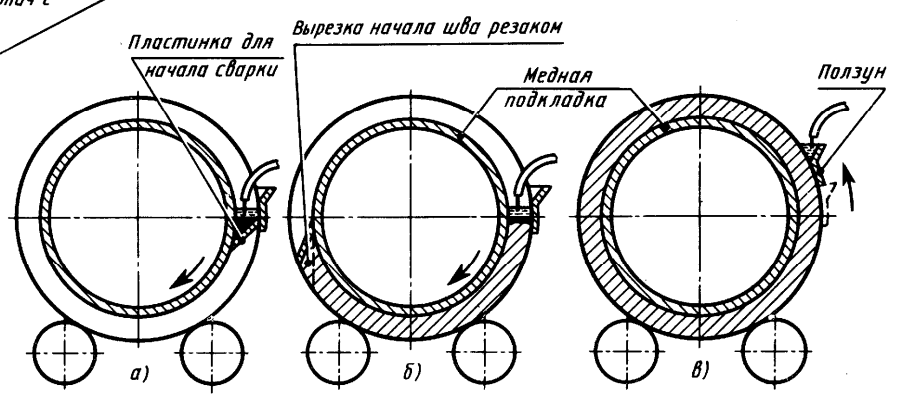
Схема электрошлаковой сварки кольцевых швов
